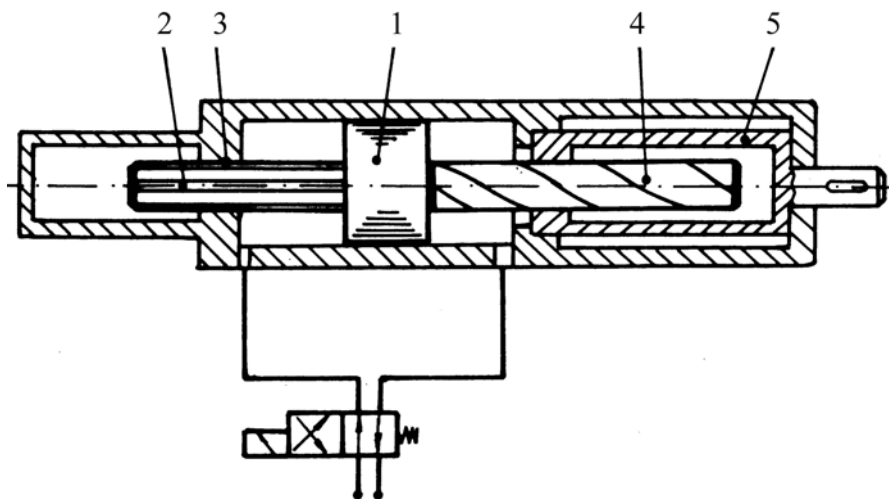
Motor hidraulic oscilant cu mecanism șurub-piuliță.
